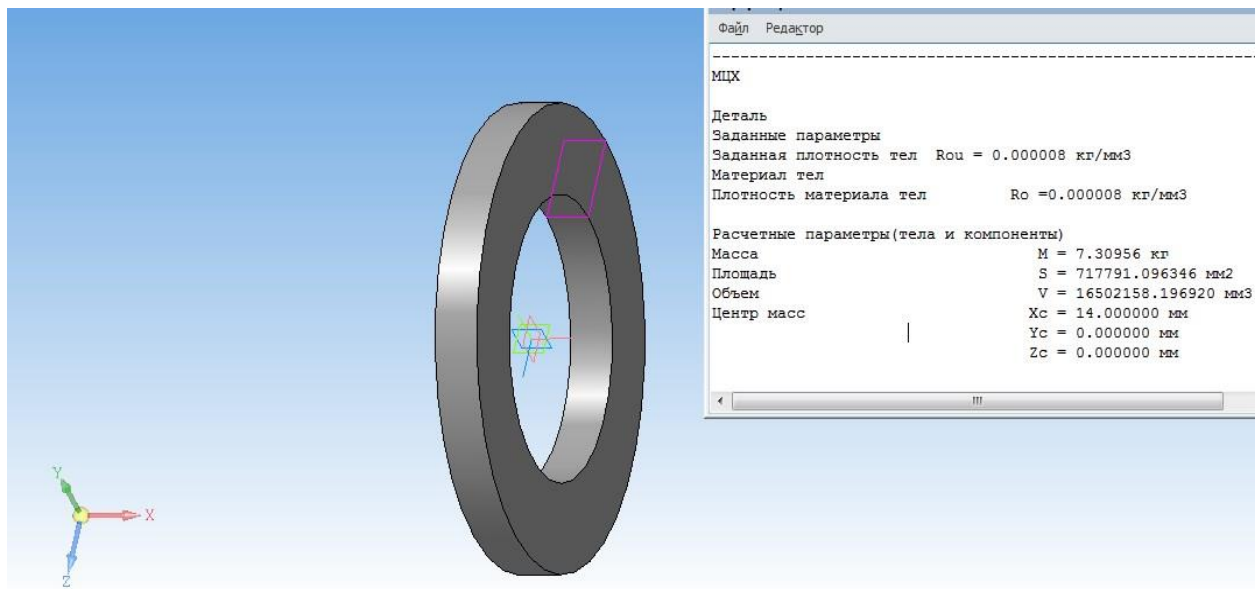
Ескіз заготовки кільце цільнокатане
